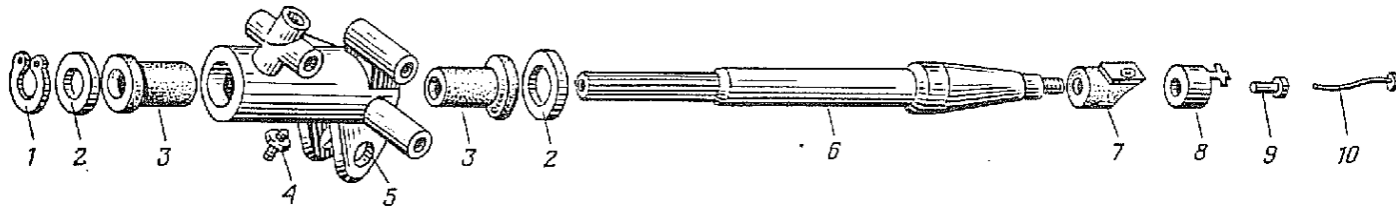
Детали вала рулевого колеса с опорой в сборе:
